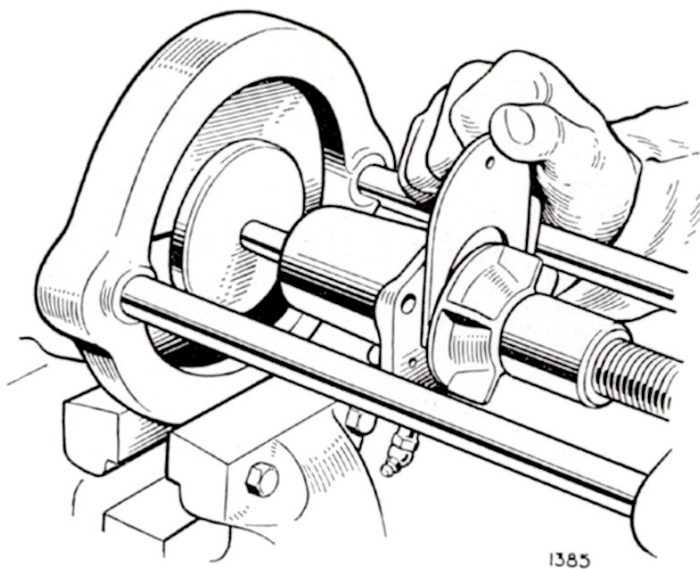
Utilisation d'une jauge d'épaisseur pour obtenir un jeu de 0,762 mm. (0,030 ") entre la turbine et la face de montage
